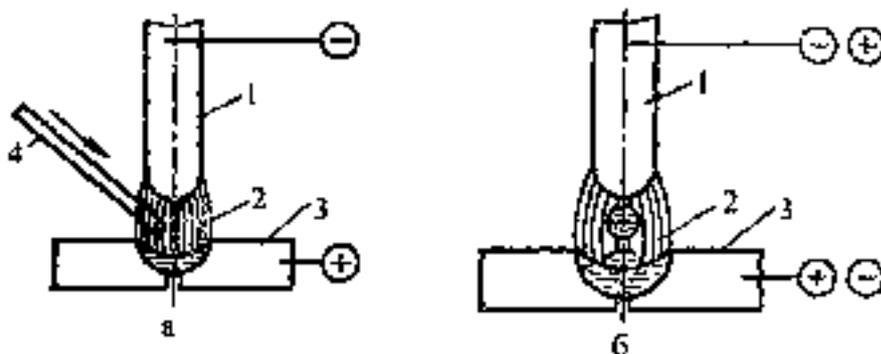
Схемы сварки неплавящимся (а) и плавящимся (б) электродами
